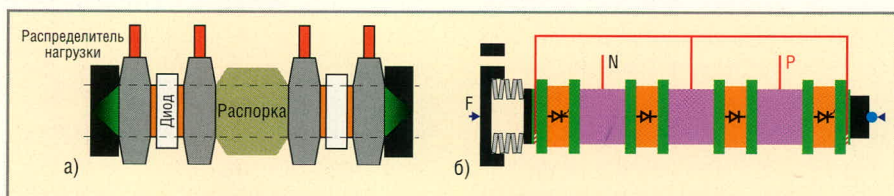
Удачно скомпонованная сборка с эффективными распределителями нагрузки и одинаковыми диаметрами приборов (а) и неудачная конструкция сборки с неэффективными распределителями нагрузки и различными диаметрами приборов (б)
